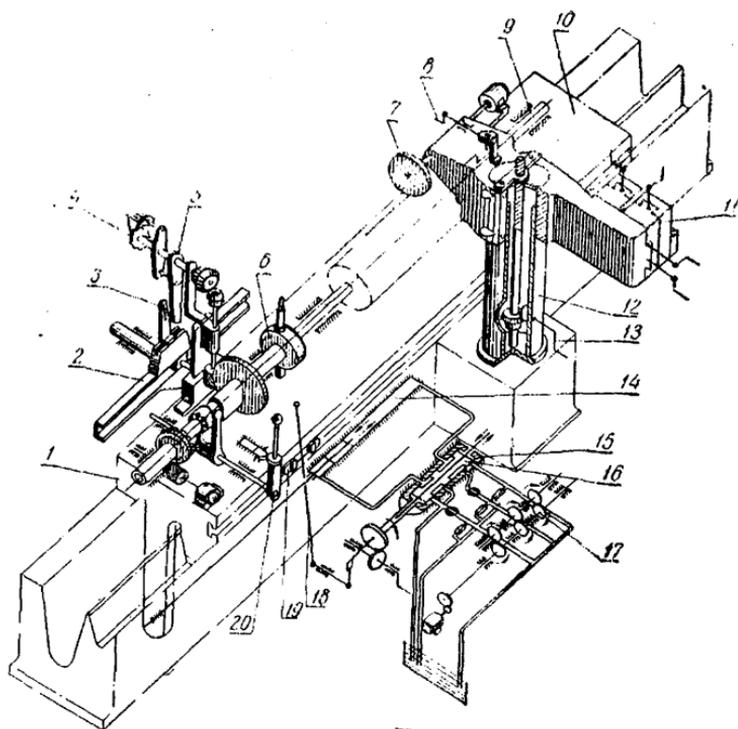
Кинематическая схема шлифовально-рифельного станка с гидромеханическим приводом:
